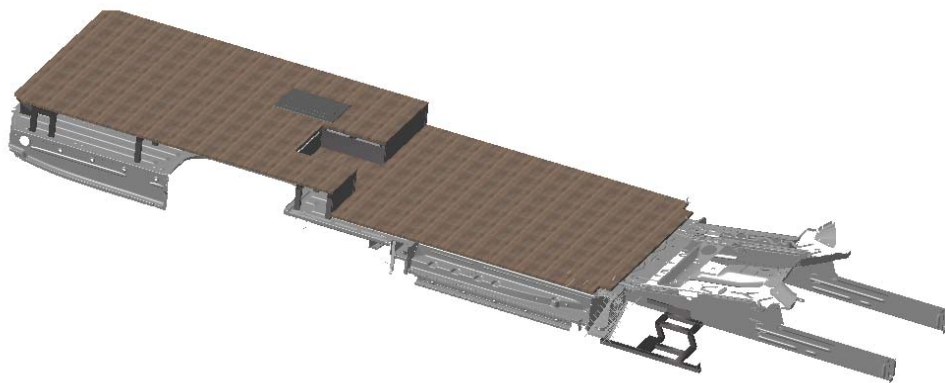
Colocación estructura estribo puerta de servicio sobre vehículo.
